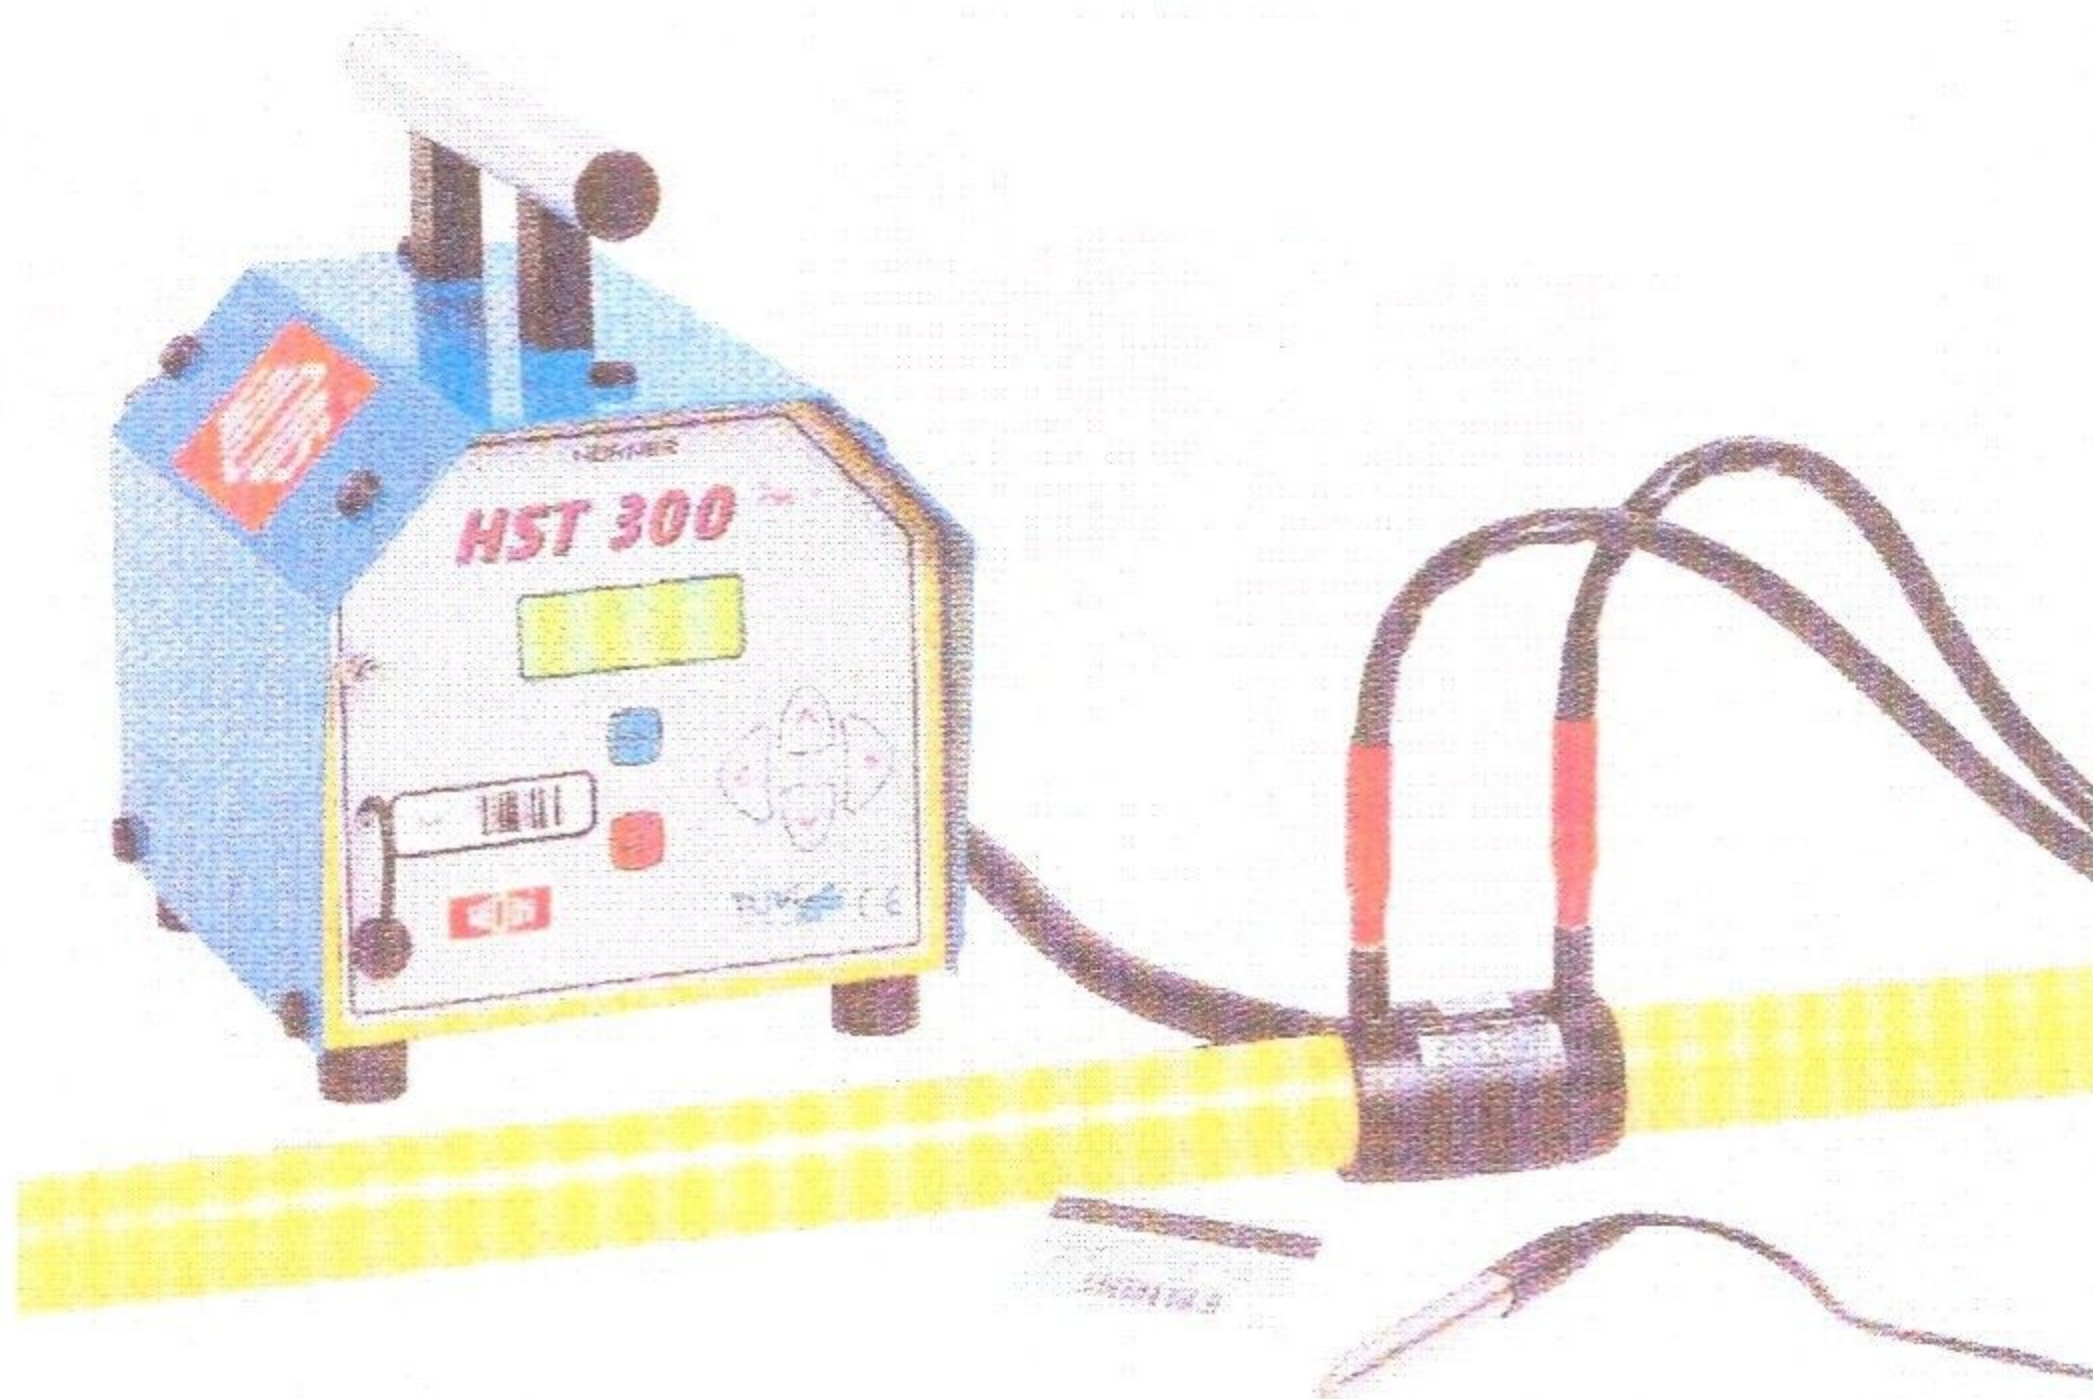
Electrosoldadura de uma tubagem em polietileno
